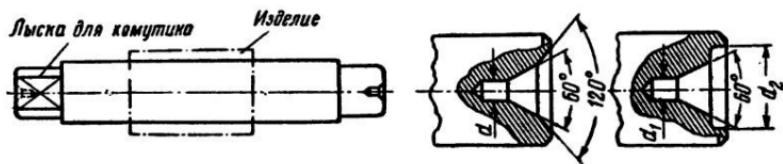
Центровая оправка. Защитные углубления ее центральных отверстий.
